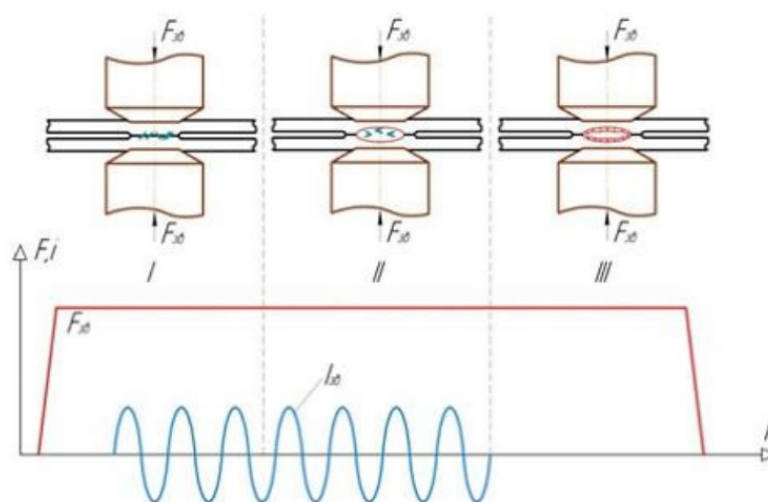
Формування з'єднань при точковому зварюванні [37]
